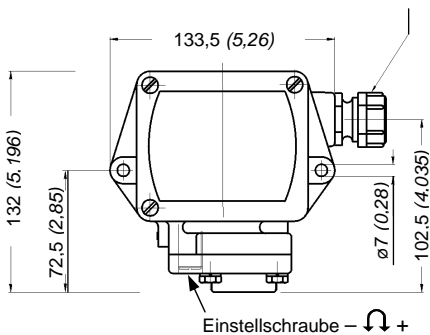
Membran-Kolben-Druckschalter Typ P1H-...
